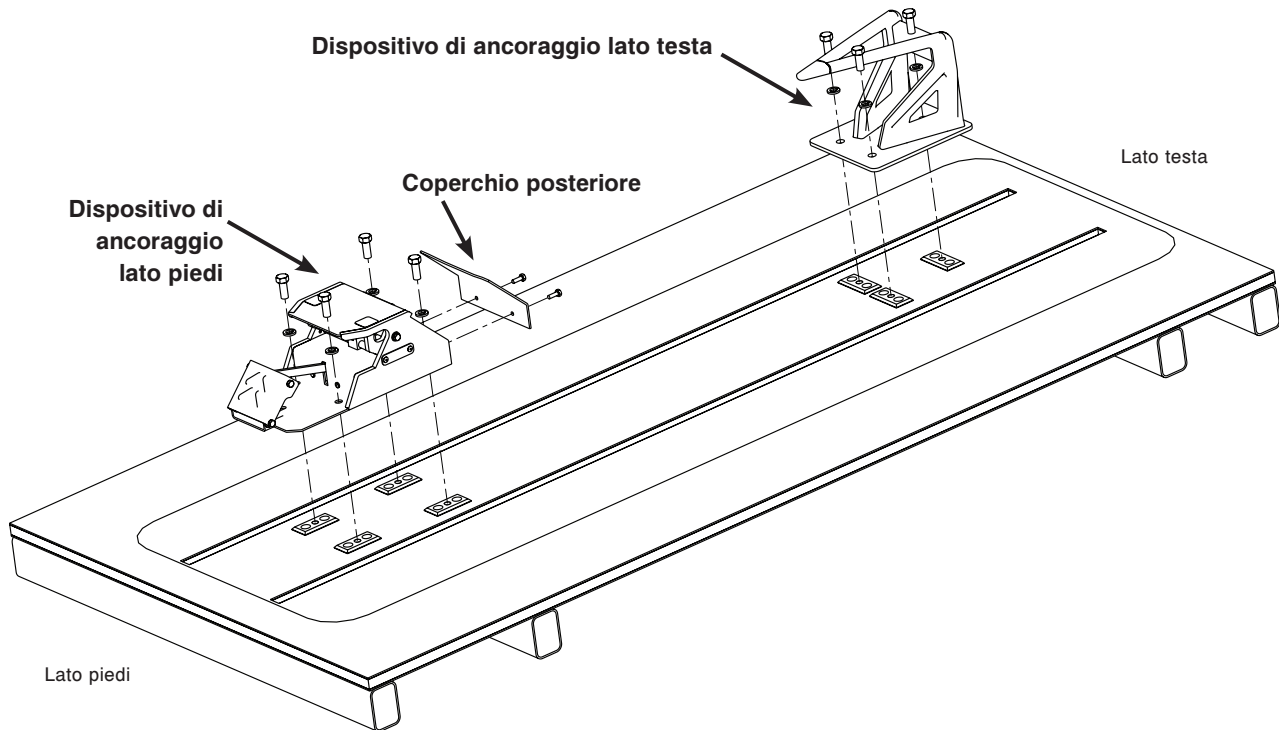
Dispositivi di ancoraggio per il lato testa e il lato piedi – Installazione della piastra a pavimento
